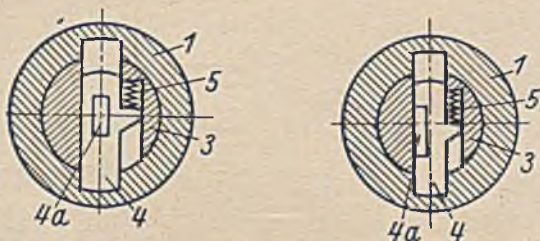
und 138. Querschnitt durch einen Schließzylinder mit einteiligen Plättchenzuhaltungen
